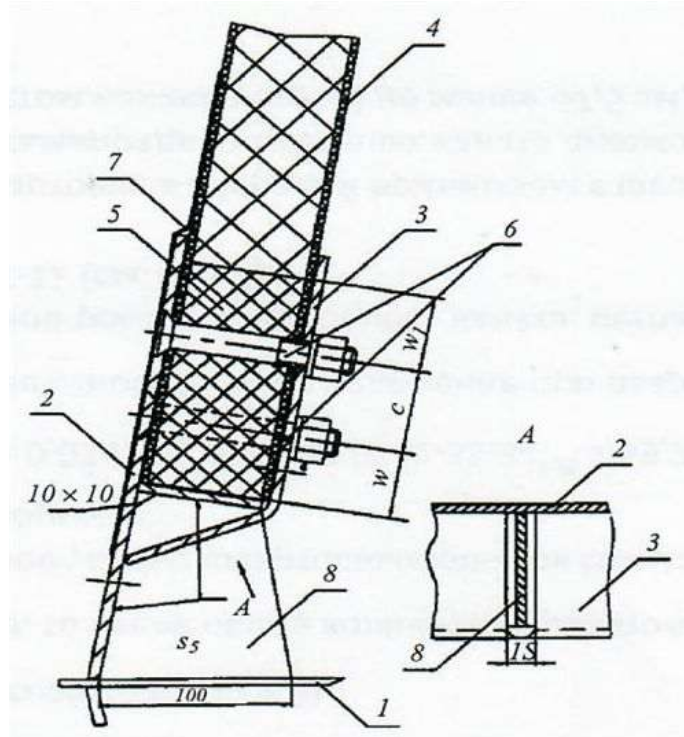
Вузол клеєболтового з'єднання панелей бортових стінок надбудови з металевим корпусом: 1 - палуба корпусу; 2 - комінгс; 3 - накладна планка; 4 - панель бортової стінки; 5 - пінопласт підвищеної густини; 6 - болти; 7 - обформовка; 8 - книця
